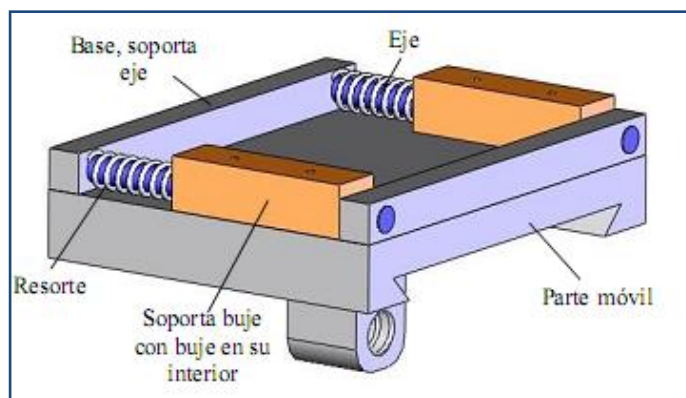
Despiece de máquina soldadora de termoplásticos.
